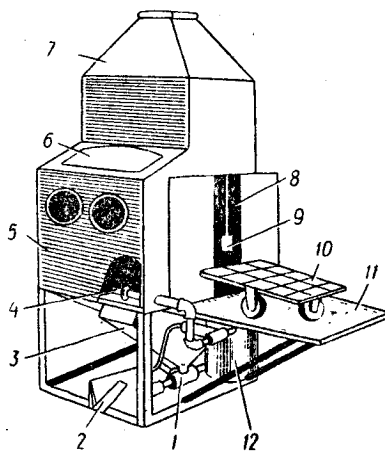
Установка для очищення деталей кісточною кришкою
